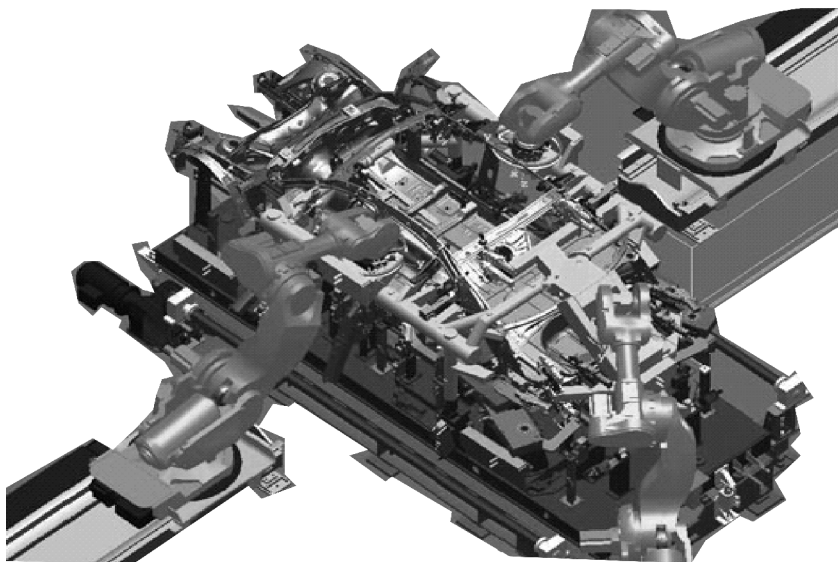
立体框架焊装夹具的 3D CAD
